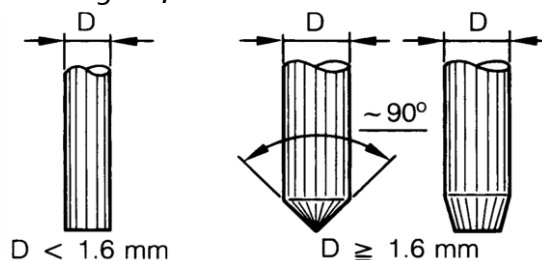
Eléctrodo de ponta para soldadura com corrente alternada
